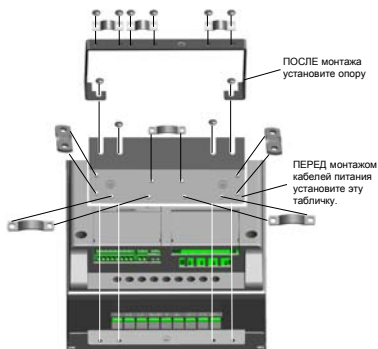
Установка заземляющей пластины и кабельных опор API, типоразмеры MI4–MI5
